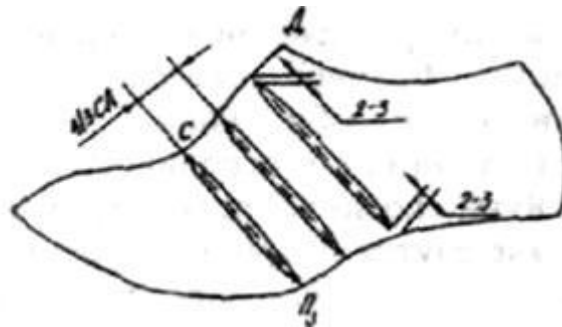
Розтин зліпку бокової поверхні колодки
